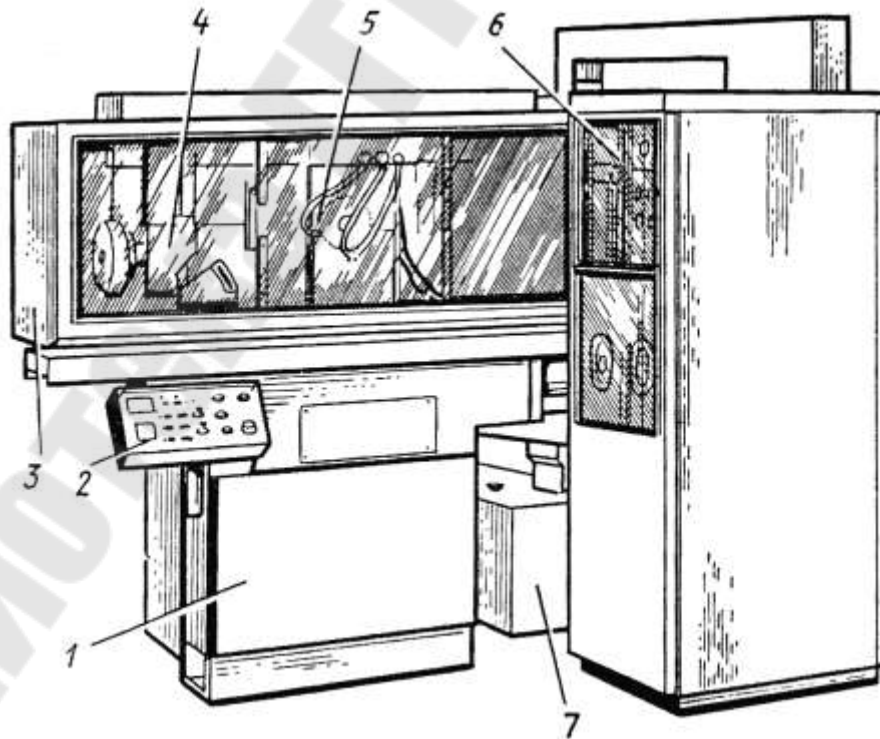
Многоцелевой заточной 4-координатный станок с ЧПУ модели ВЗ-205ФЗ: 1 – станина; 2 – пульт управления; 3 – кожух; 4 – бабка изделия; 5 – шлифовальная бабка; 6 – устройство ЧПУ; 7 – бак СОЖ
